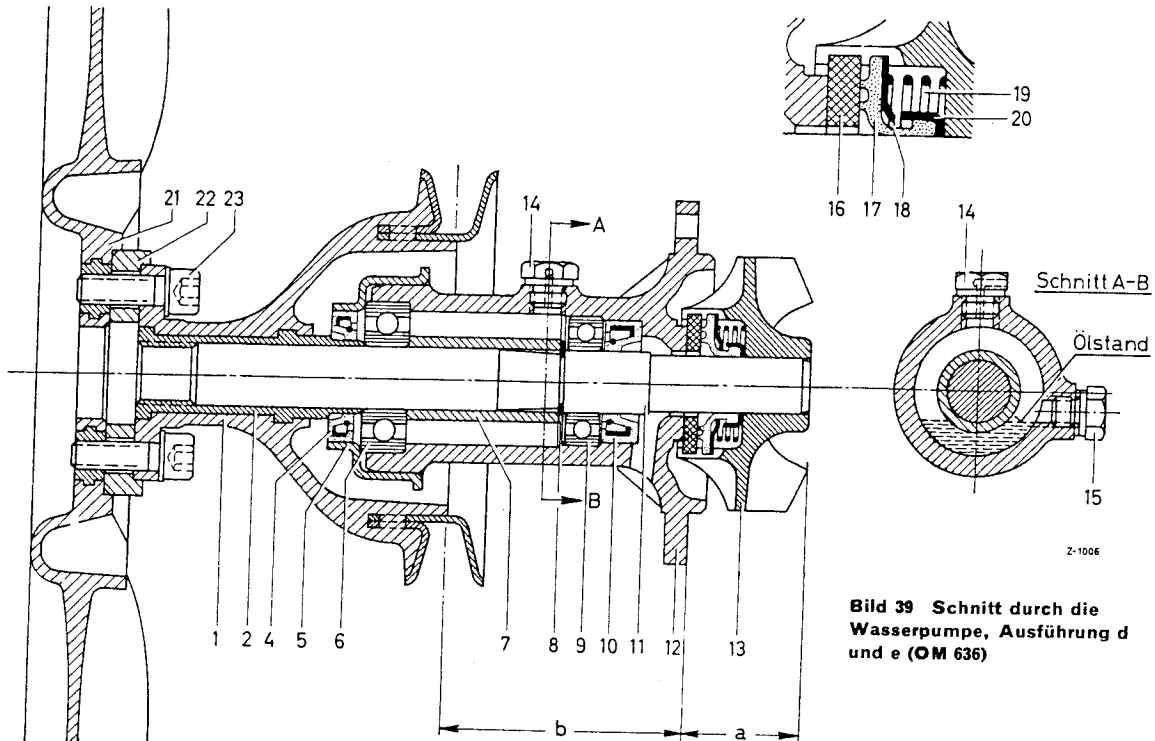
Schnitt durch die Wasserpumpe, Ausführung d und e (OM 636)
